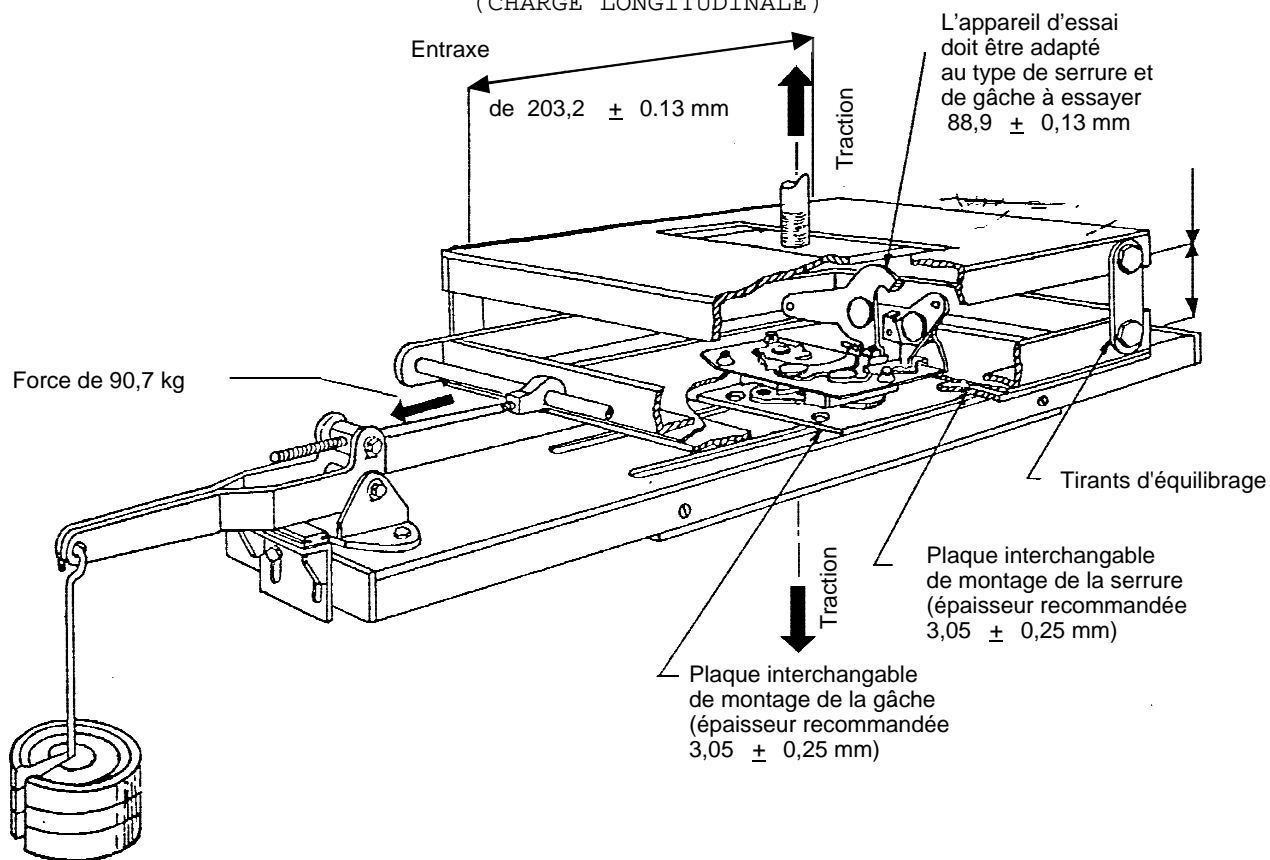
SERRURES DE PORTES - DISPOSITIF D'ESSAI
